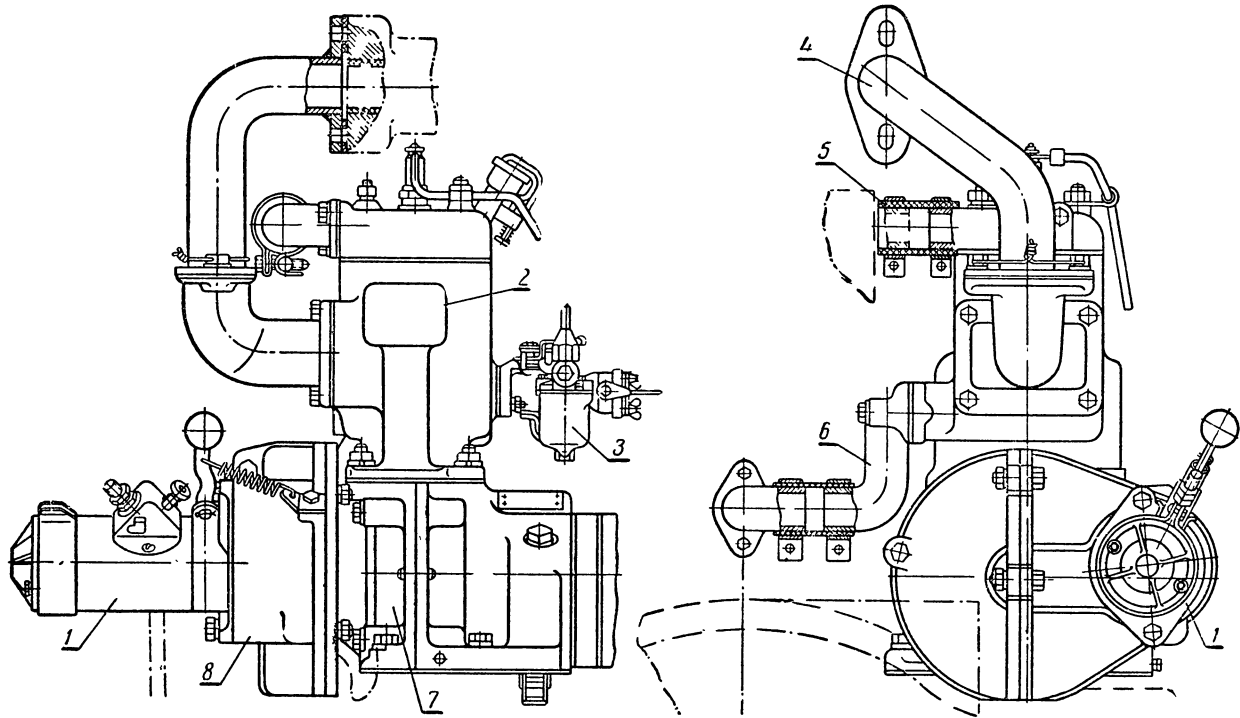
Пусковой двигатель ПД-10М-1 со стартером дизеля Д-75 (общий вид):
